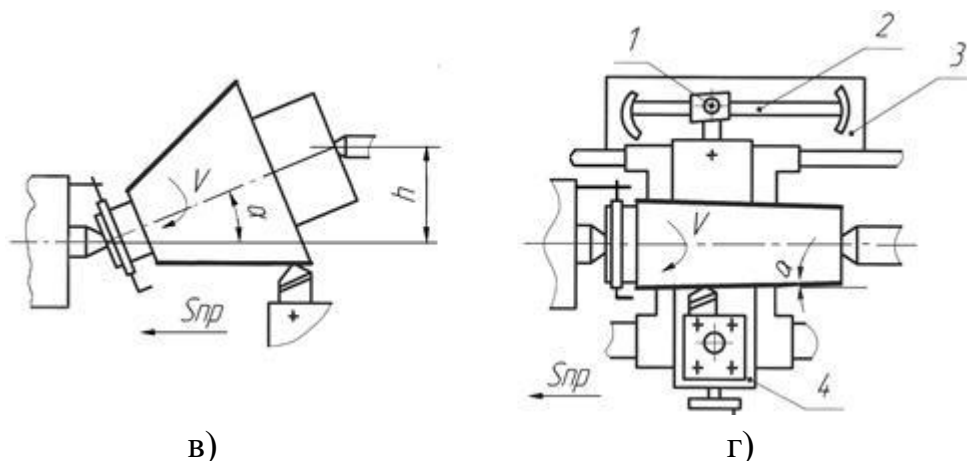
Схемы обработки конических поверхностей на токарно-винторезном станке
